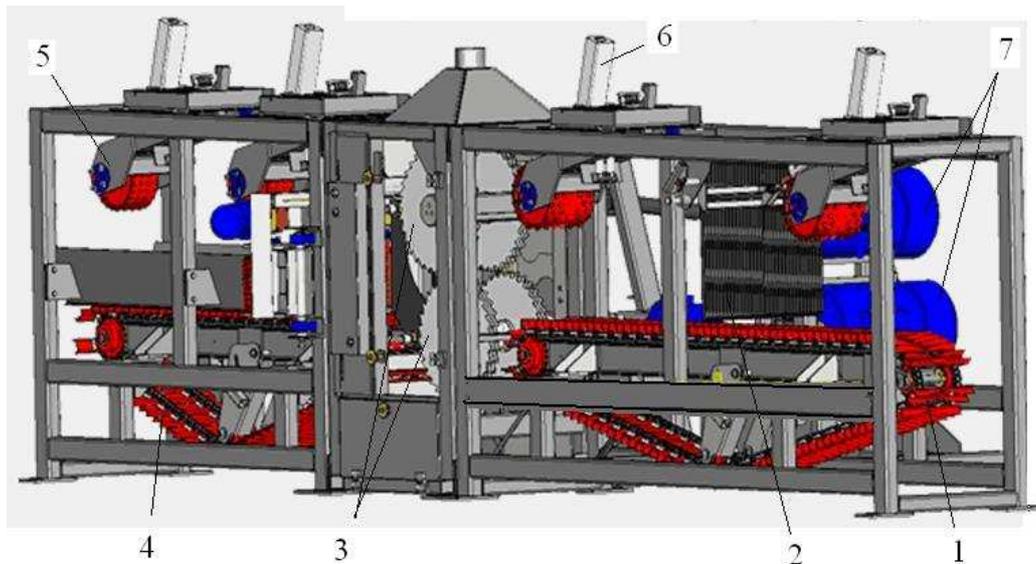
Головной бревнопильный двухвальный станок модели Ц16Б2 «KRAFTER»:
